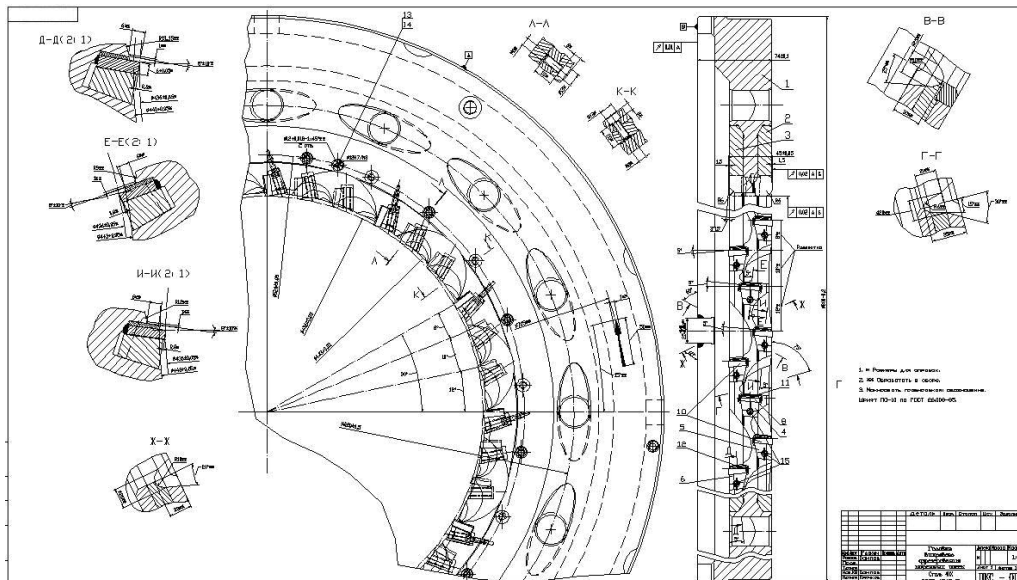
Чертеж головки для вихревого фрезерования коренных опор.
